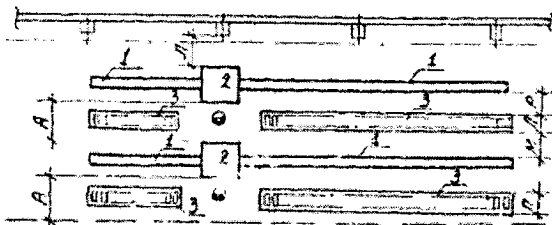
Розміщення устаткування для зварювання довгомірних деталей :
